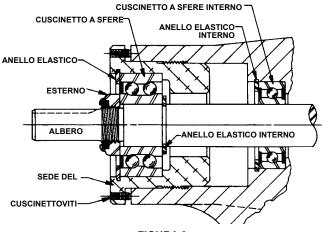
ASSEMBLAGGIO DEL REGGISPINTA GG,HJ E HL
